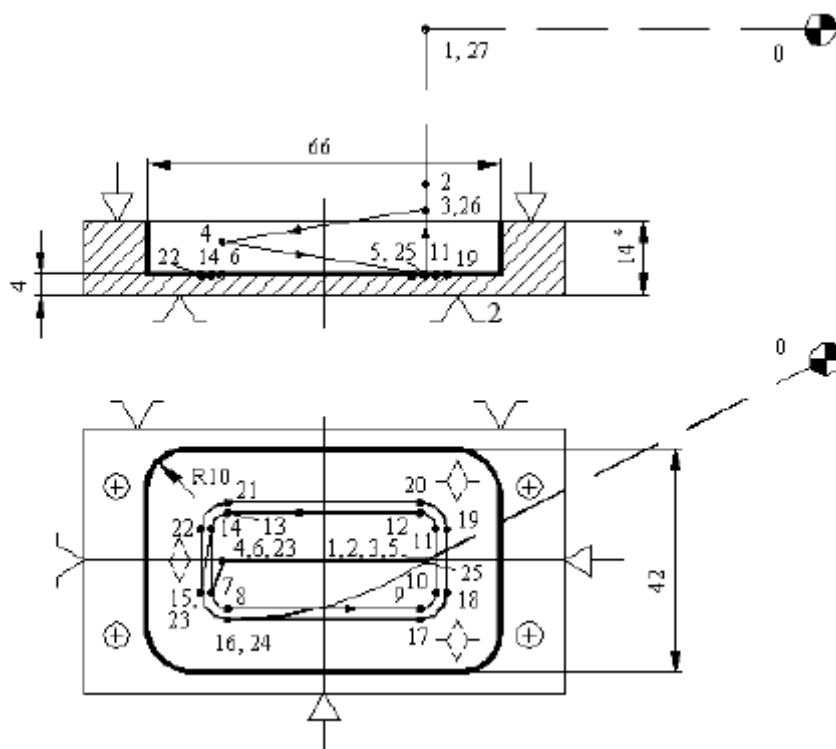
Траєкторія руху фрези при обробці внутрішнього контуру
